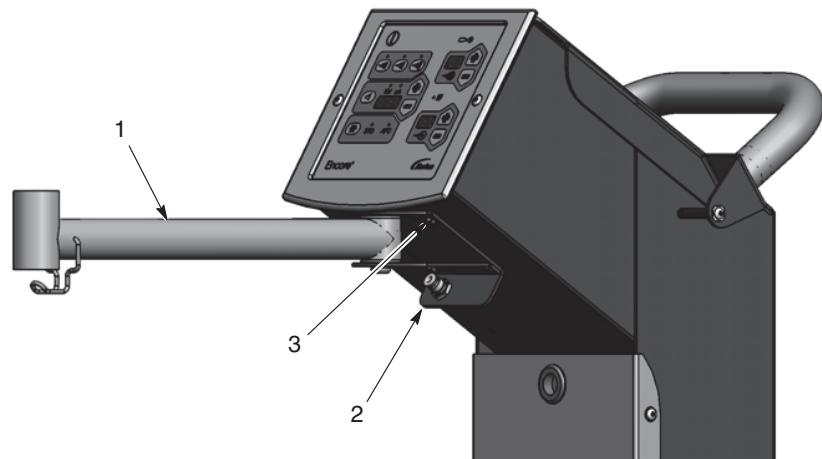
Připojení řídicí jednotky pistole Encore LT
